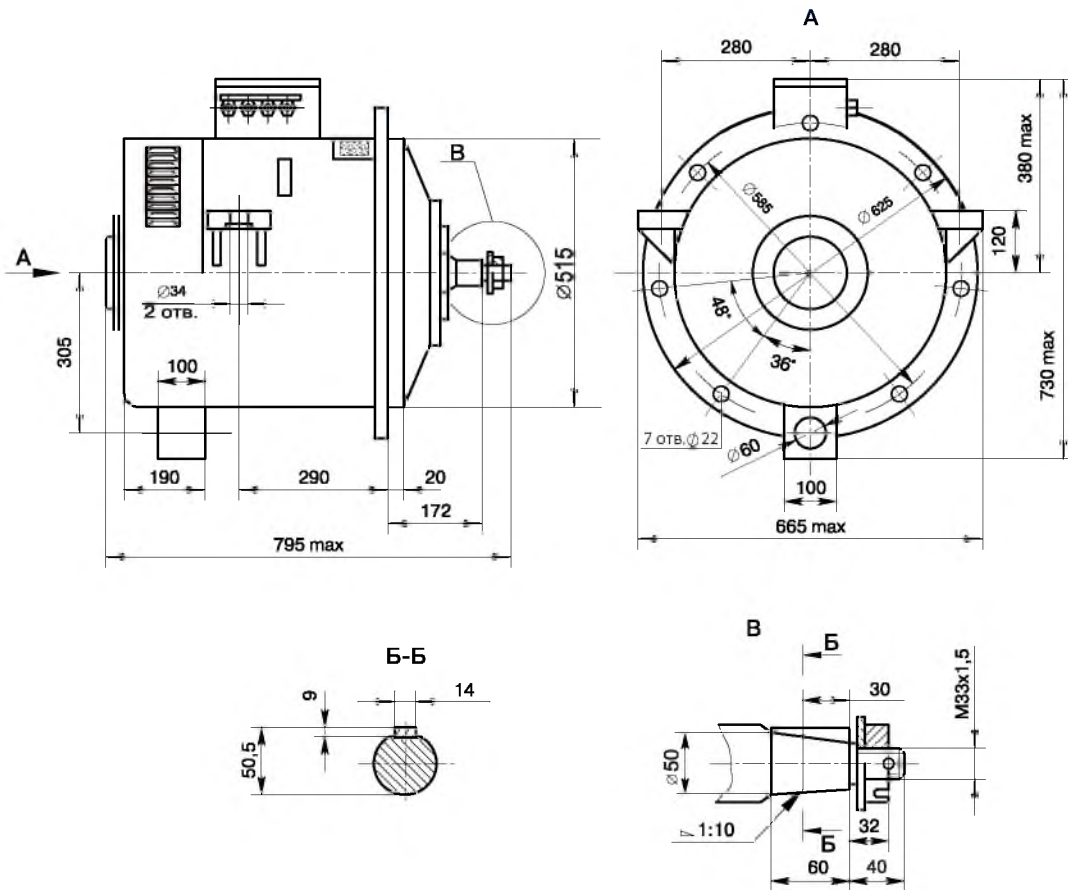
Габаритные и установочные размеры электродвигателя ДТН-45/27
